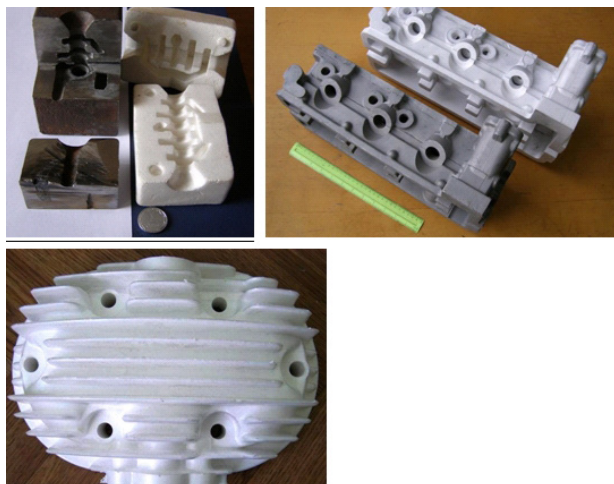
Отливки и модели деталей гидропаратуры, двигателей и др. корпусное литье
